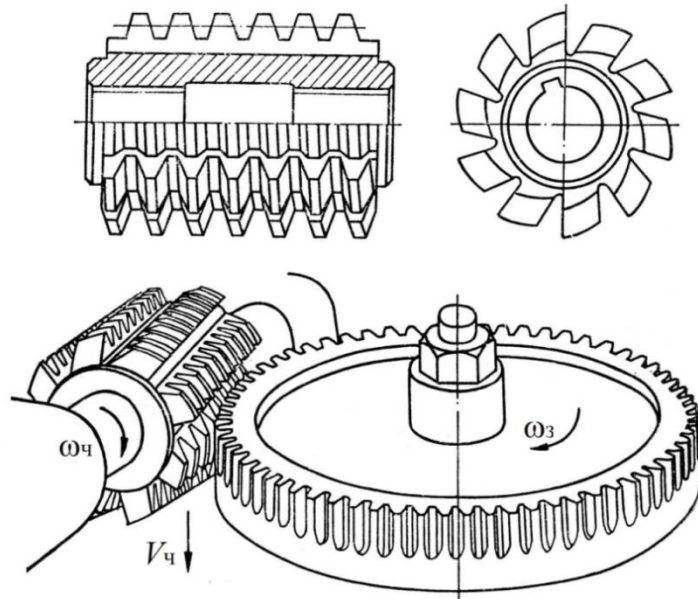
Нарізування зубчастого колеса черв'ячною фрезою
